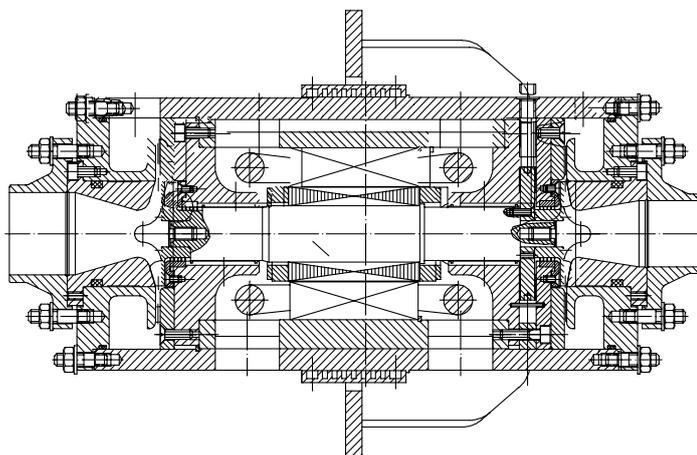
Двухступенчатый холодильный центробежный компрессор со встроенным электродвигателем и газодинамическими подшипниками (ВНИИХолодмашхолдинг, г. Москва)
